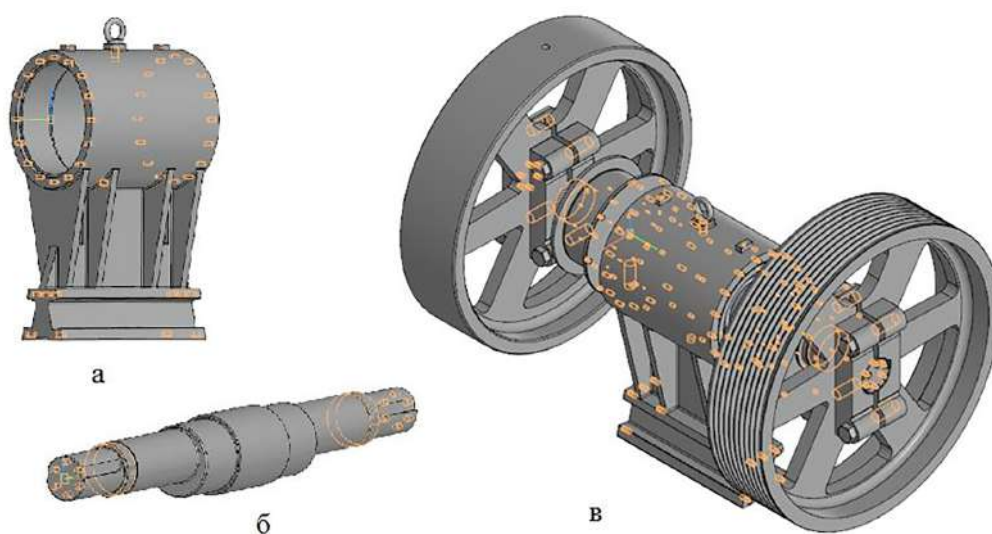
Модели некоторых деталей и сборки узла главного вала:
